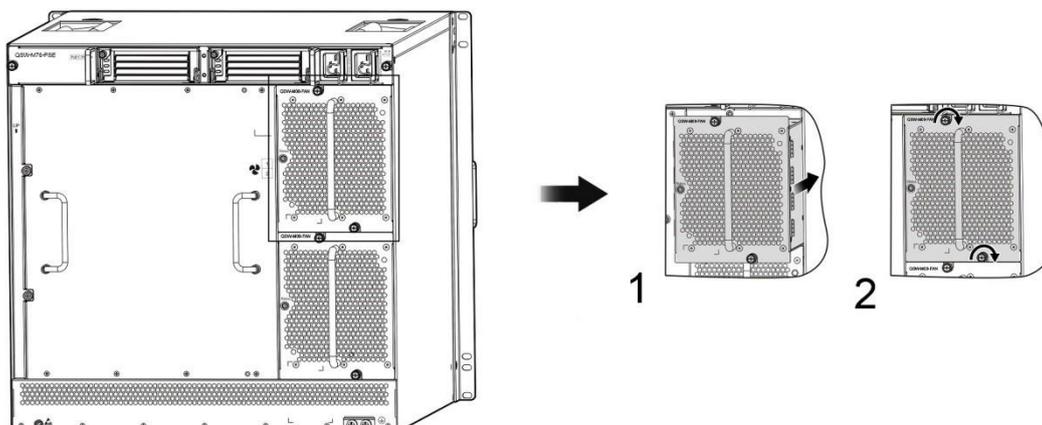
Установка корзины для вентиляторов QSW-M08-FAN
